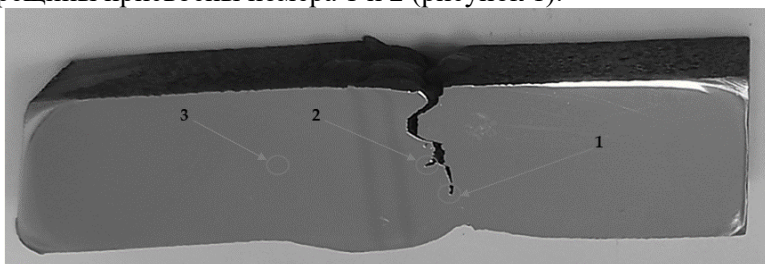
Боковая поверхность образца №1 после процессов шлифовки и полировки
